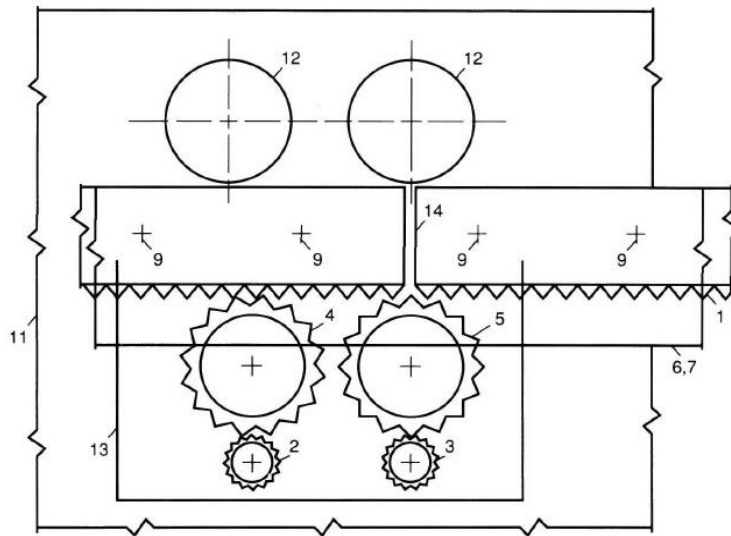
Mecanismo de rodas e engrenagens para locomoção de uma carruagem. Retirado de [5].
